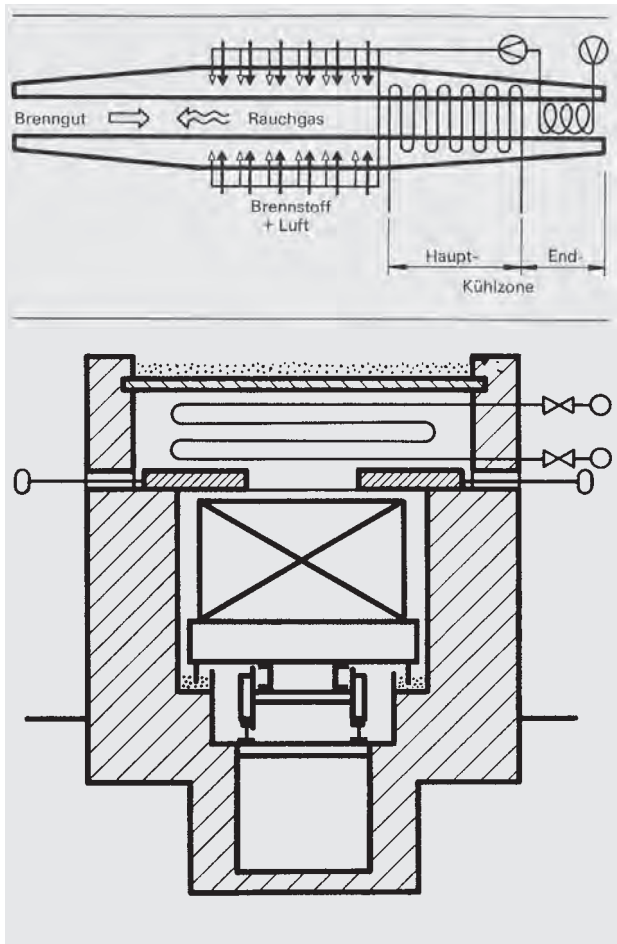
Tunnelofen, System Dr. Cremer. Oben schematische Darstellung, unten Schnitt durch die Hauptkühlzone
